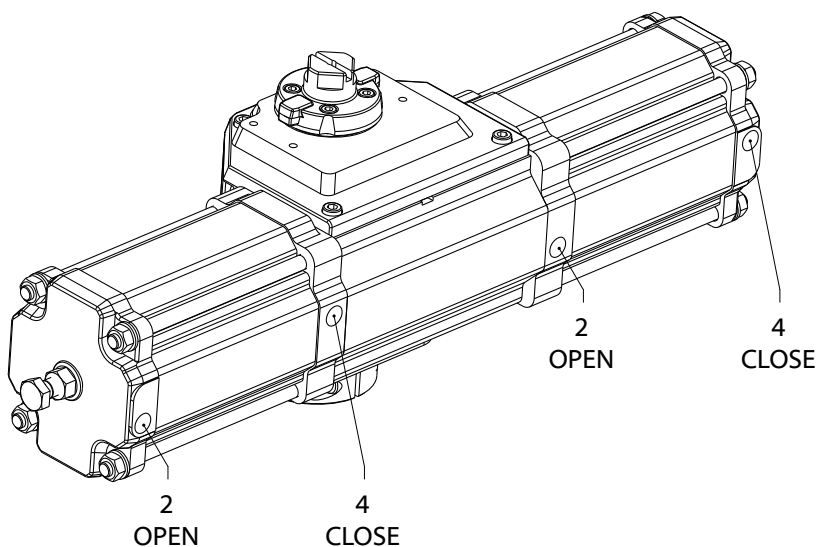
Пневматическое соединение в типе А размер A22, 32... с двумя цилиндрами
